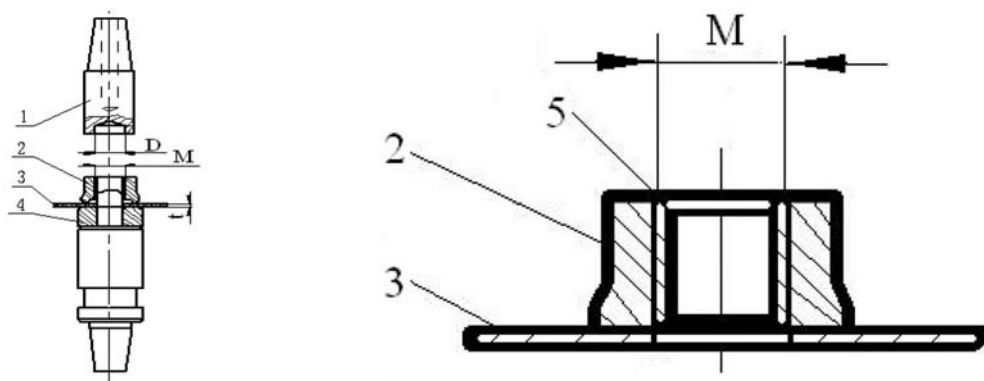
Конструкция электрода для сварки высокопрочной гайки с выступом: 1 – верхний электрод; 2 – привариваемая гайка; 3 – листовая деталь; 4 – нижний электрод; 5 – фаска отверстия привариваемой гайки
